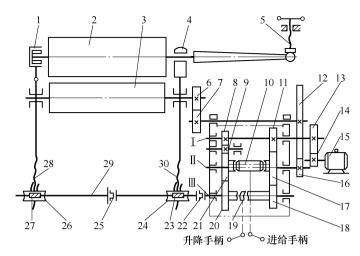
对称式三辊滚板机传动系统 1—活动轴承 2—上轴辊 3—下轴辊 4—固定轴承 5—平衡螺杆 6、7、8、9、11、12、13、14、16、17、18、20、21—齿轮 10—摩擦式离合器 15—电动机 19—啮合式离合器 22、25—联轴器 23、27—蜗杆 24、26—蜗轮 28、30—升降丝杠 29—蜗杆轴
